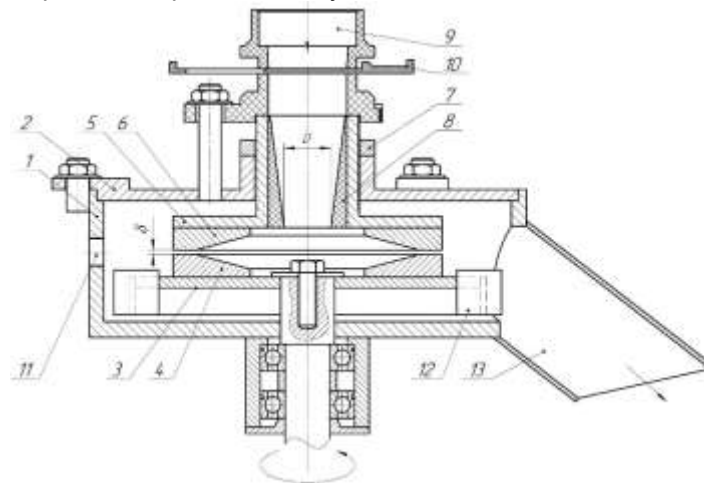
Схема експериментального дискового подрібнювача зерна: 1 – робоча камера; 2 – верхня кришка робочої камери; 3 – тримач нижнього обертового диска; 4 – нижній обертовий диск; 5 – тримач верхнього нерухомого диска; 6 – верхній нерухомий диск; 7 – контр-гайка механізму встановлення модульного зазору; 8 – змінна втулка встановлення подачі матеріалу; 9 – завантажувальна горловина; 10 – шиберна засувка; 11 – отвір для встановлення модульного зазору; 12 – лопать; 13 – патрубок для відводу подрібненого продукту
